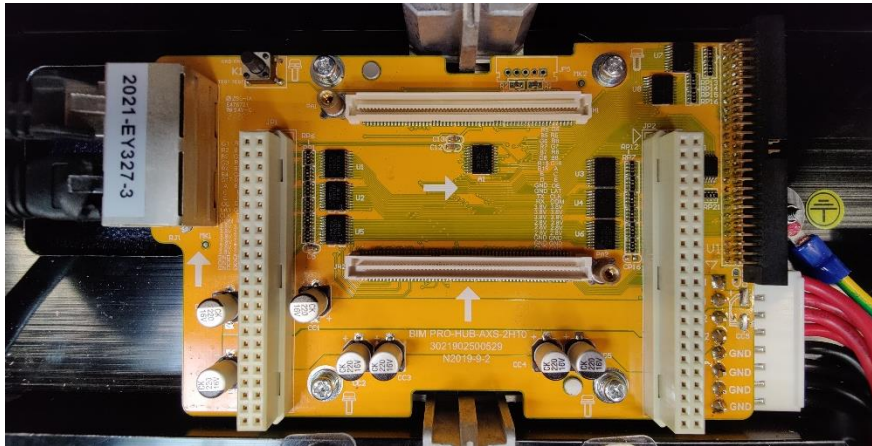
Hub Board mit allen Anschlüssen auf einer Seite⁵
